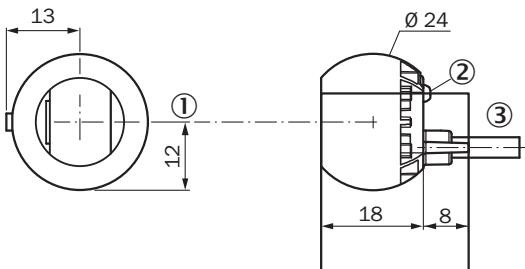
ZSE18-3xxxxx/ZTx18-Cxxxxx
